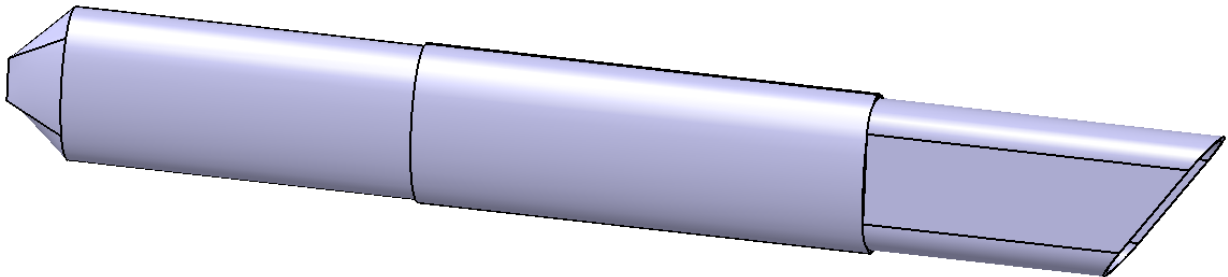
Strut*-pieza 1: Resultado de soldadura 1
